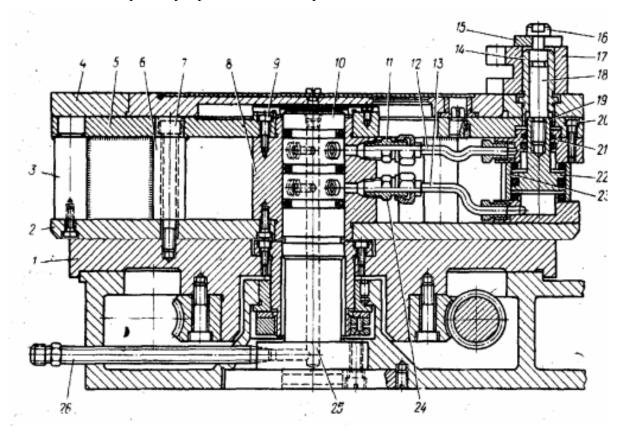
Многоместное приспособление с гидроприводом для фрезерных станков с вращающимся столом
